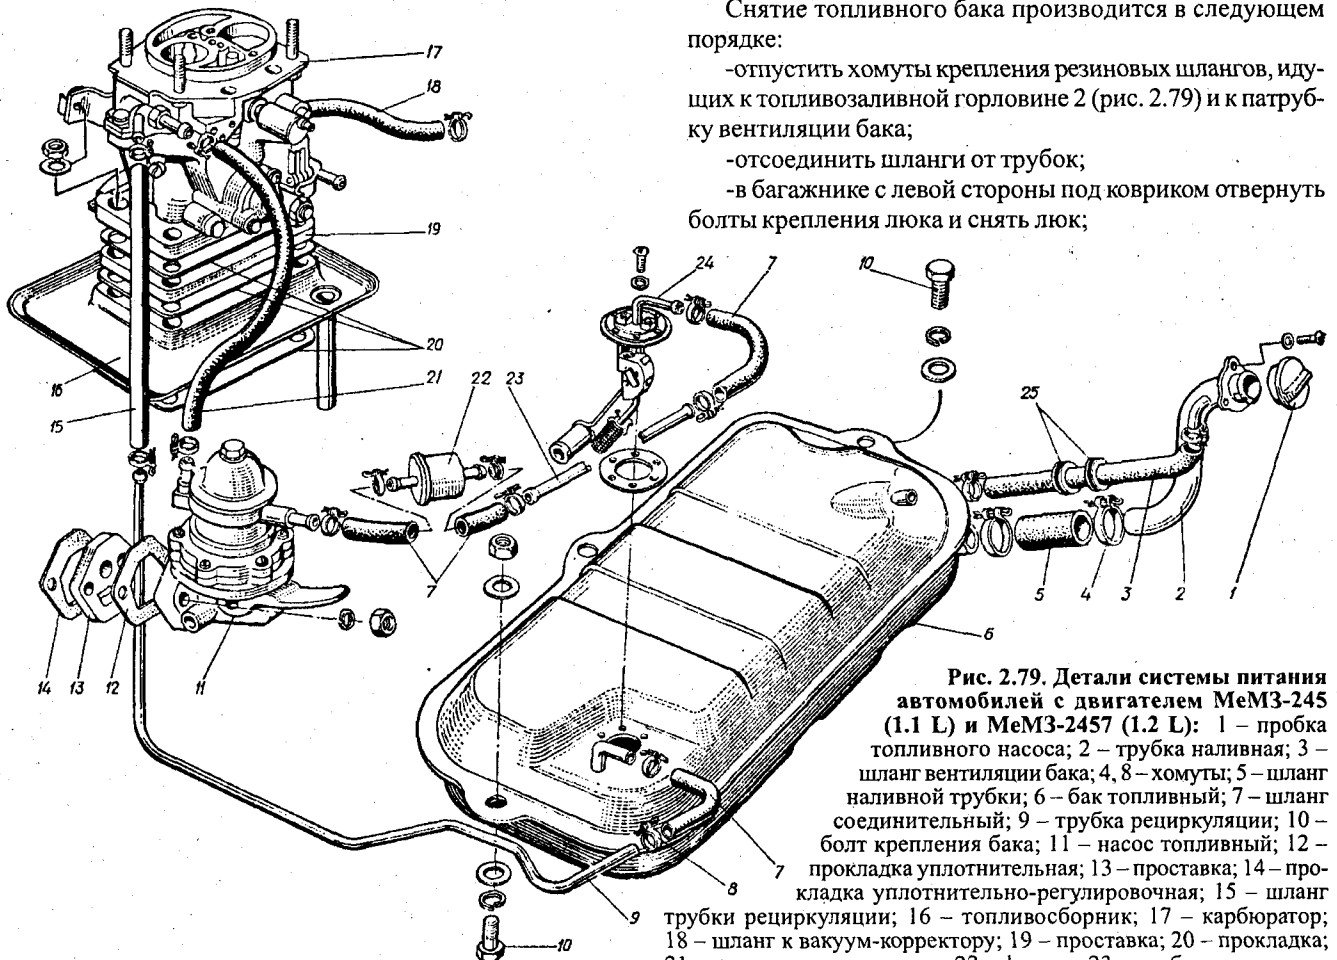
Детали системы питания автомобилей с двигателем МЕМ3-245 (1.1 L) и МЕМ3-2457 (1.2 L): 1 - пробка топливного насоса; 2 - трубка наливная; 3 - шланг вентиляции бака; 4, 8 - хомуты; 5 - шланг наливной трубки; 6 - бак топливный; 7 - шланг соединительный; 9 - трубка рециркуляции; 10 - болт крепления бака; 11 - насос топливный; 12 - прокладка уплотнительная; 13 - проставка; 14 - прокладка уплотнительно-регулирующая; 15 - шланг трубки рециркуляции; 16 - топливосборник; 17 - карбюратор; 18 - шланг к вакуум-корректору; 19 - проставка; 20 - прокладка; 21 - шланг подачи топлива; 22 - фильтр; 23 - трубка подачи топлива; 24 - датчик уровня бензина; 25 - втулка уплотнительная
